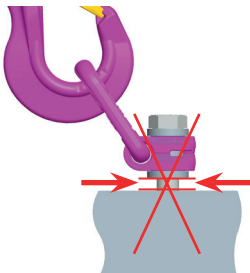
L'anneau d'arrimage doit être entièrement vissé.
